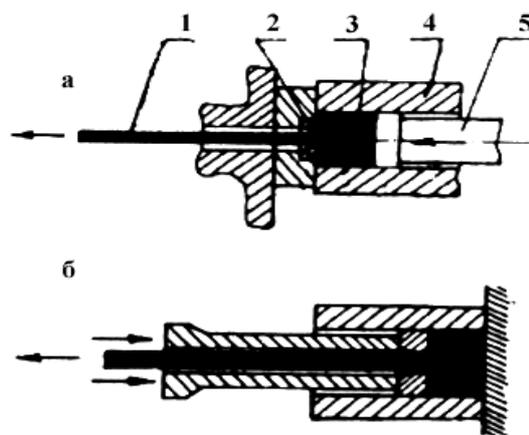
Схемы прессования: а – прямой метод; б – обратный (1 – пруток; 2 – матрица; 3 – нагретый слиток; 4 – контейнер; 5 – пуансон)
